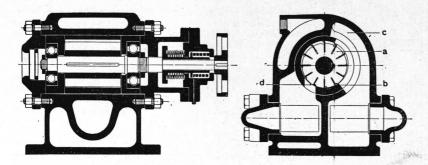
Cortes del compresor rotativo "Frigorotor"
